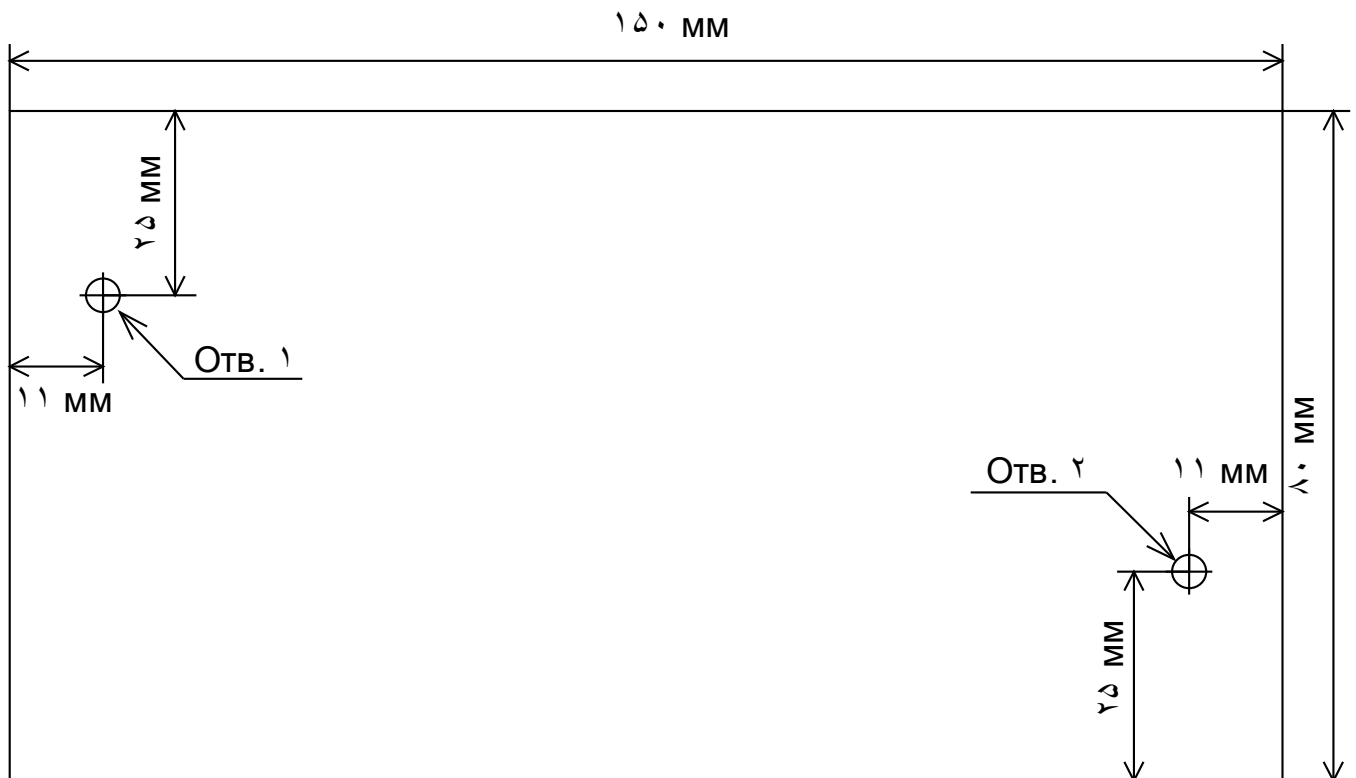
Разметка крепежных отверстий для установки преобразователя.
